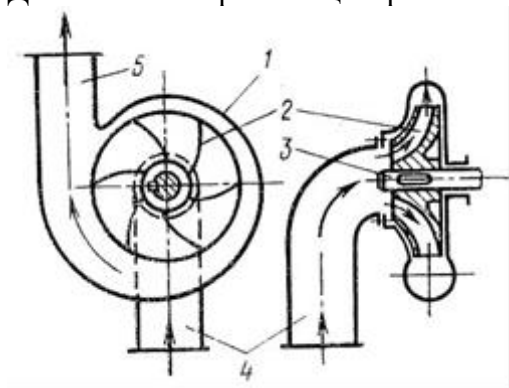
Схема центробежного насоса: 1 - корпус; 2 - рабочее колесо; 3 - вал; 4 - всасывающий трубопровод; 5 - нагнетательный трубопровод.
